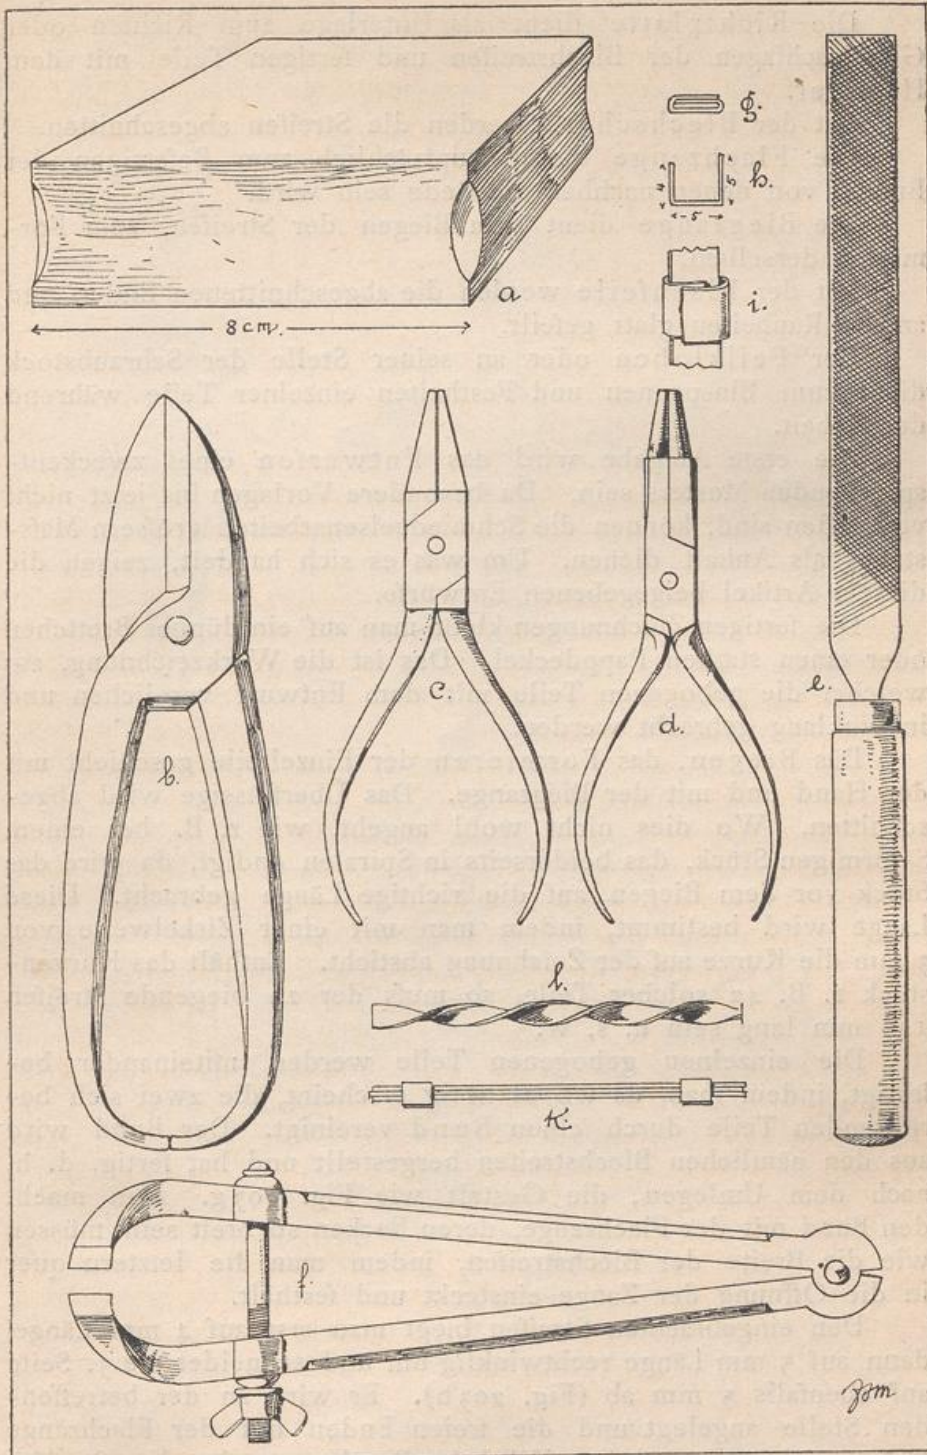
Werkzeuge für die Klein-Eisen-Arbeit.
